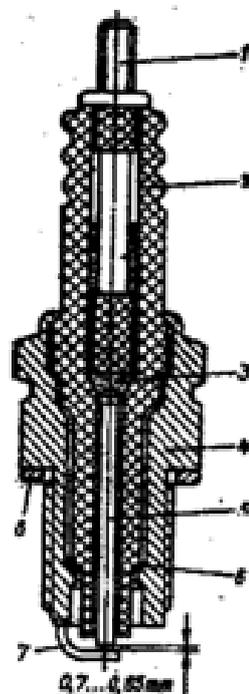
Свеча зажигания: 1 - контактная головка; 2 - изолятор; 3 - токопроводящий герметик; 4 - корпус ($S = 21$ мм); 5 - центральный электрод; 6 - теплоотводящая шайба; 7 - боковой электрод; 8 - прокладка
